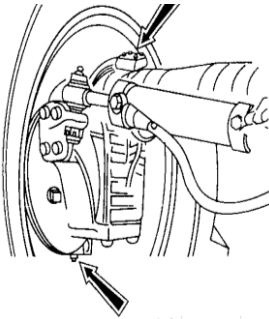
Смазка подшипников опор шкворня колесного редуктора и втулок оси качания переднего ведущего моста
